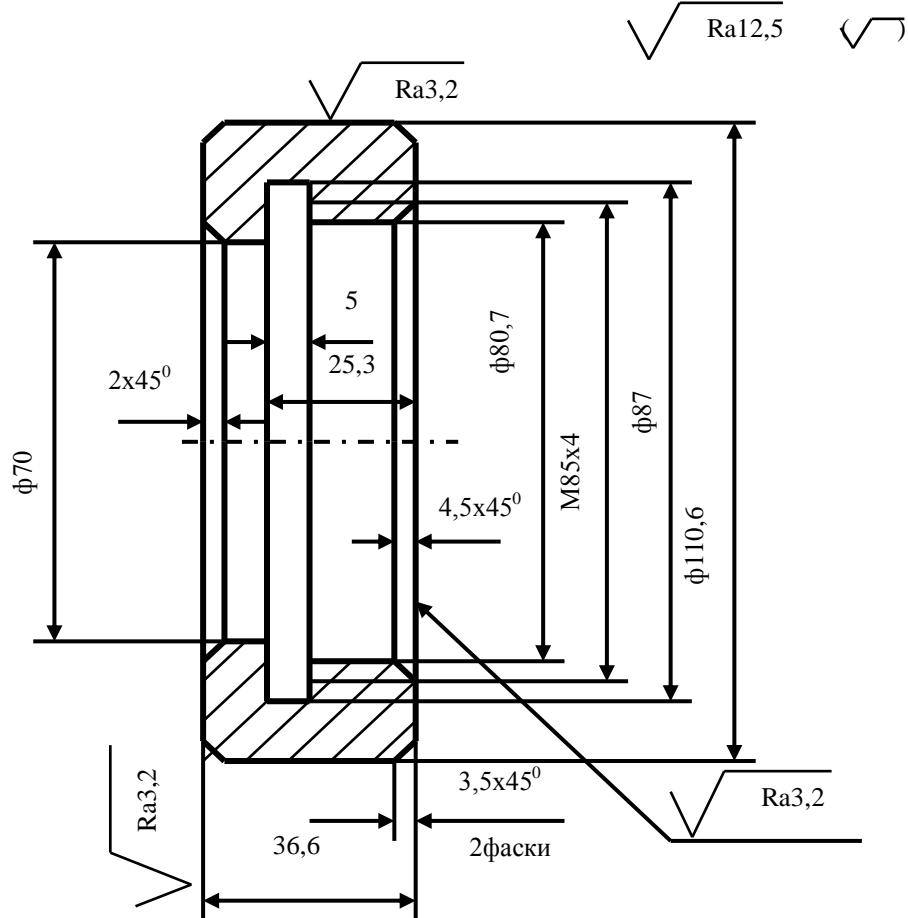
Чертеж токарной заготовки (оформляется на формате А4)
